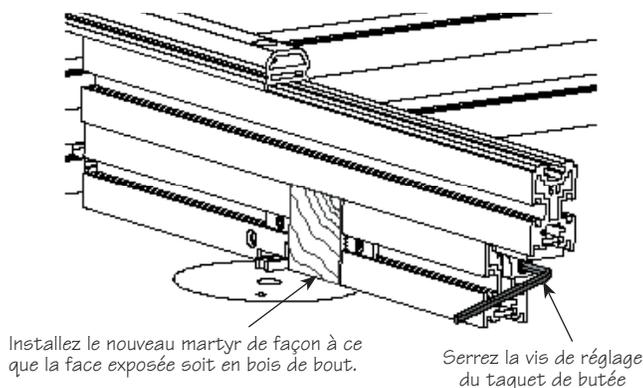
Installez le nouveau martyr (face exposée en bois de bout) et serrez la vis de réglage du taquet de butée.
